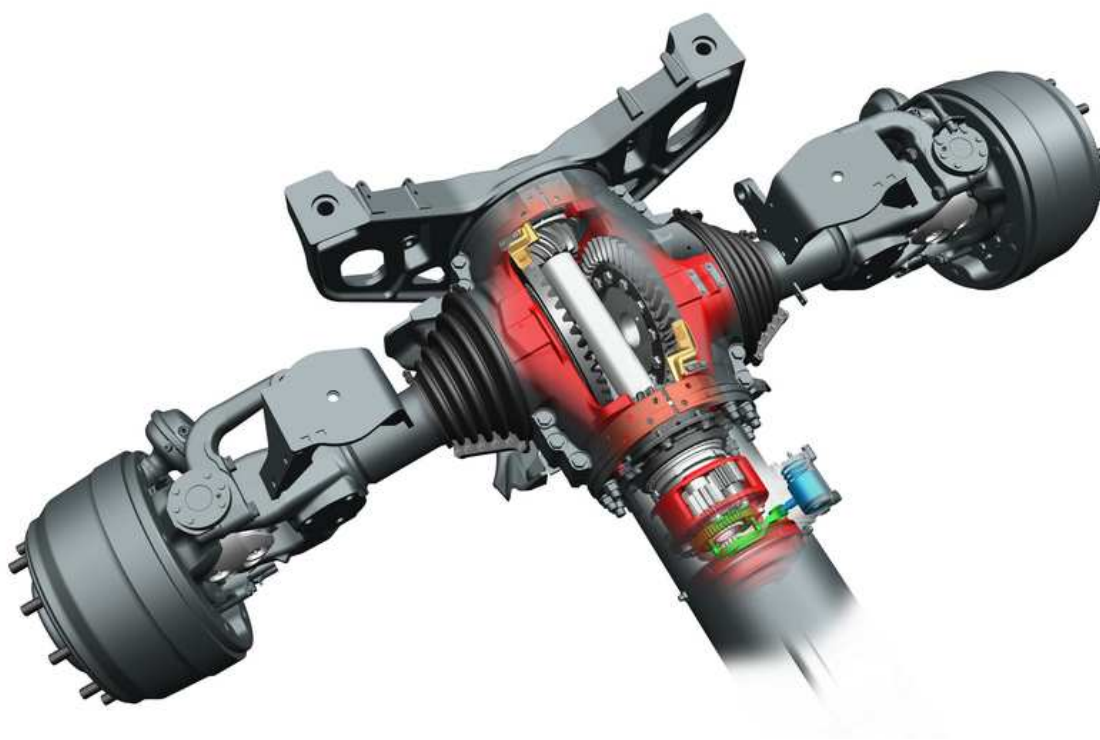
Základní uspořádání pohonu zadní nápravy vícenápravových vozidel [3]
